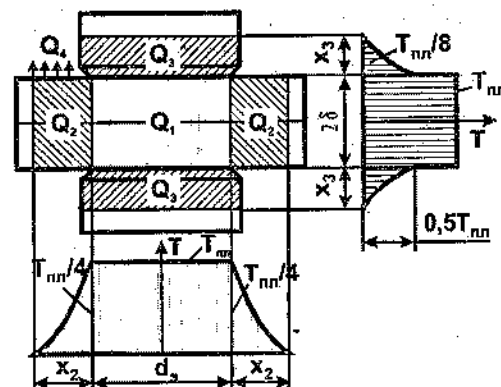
Характер нагрева деталей одинаковой толщины при точечной сварке
